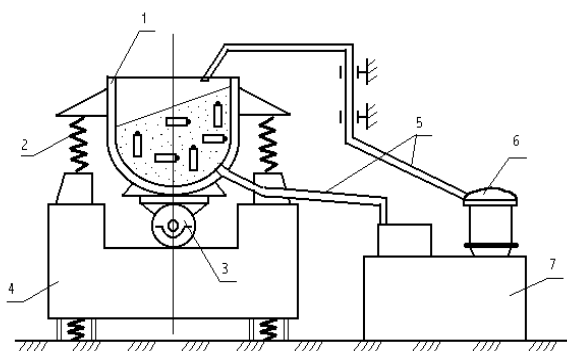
Схема станка для ВиОУО: 1 – рабочая камера; 2 – упругий элемент; 3 – дебалансный вибратор; 4 – основание; 5 – шланги для подачи и слива технологической жидкости; 6 – pompa; 7 – бак-отстойник
